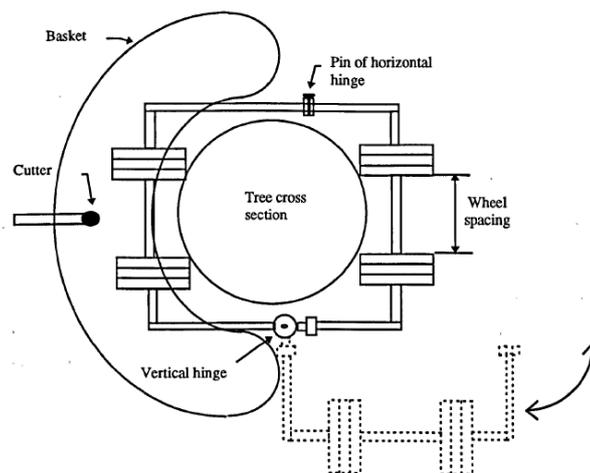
Vue de dessus de la machine (Shamsi, 1998).
